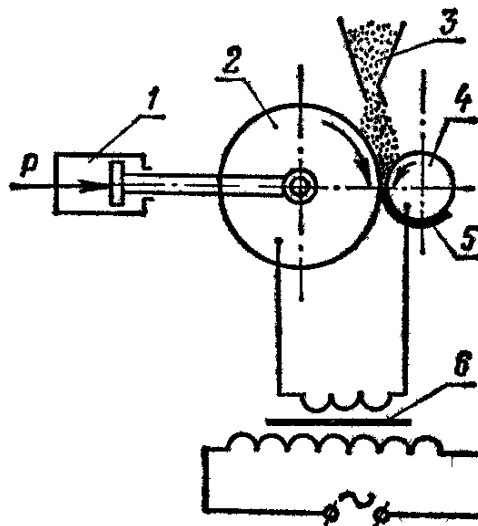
Схема процесу електроконтактного напикання металевих порошків: P — притискне зусилля; 1 – пневмоциліндр; 2 – притискний ролик; 3 – металевий порошок; 4 – відновлювана деталь; 5 – напечений шар; 6 – трансформатор
